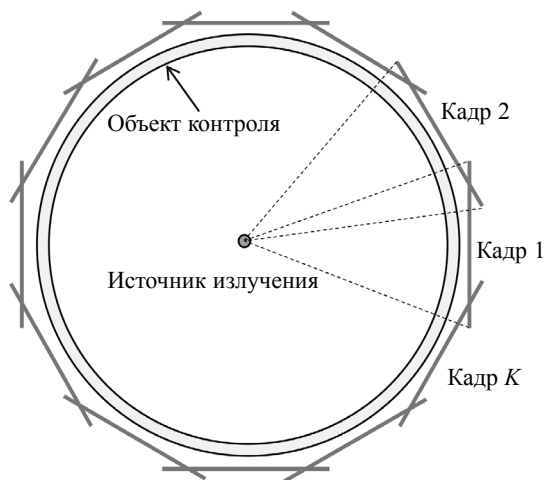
Схема радиографического контроля сварного шва.
